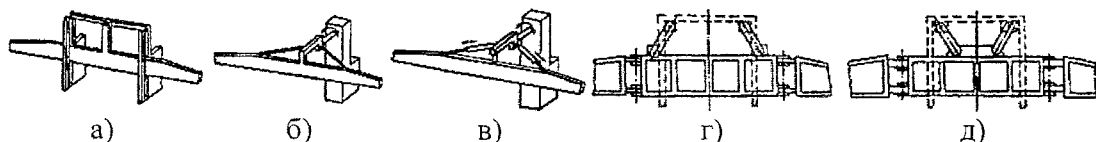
Подвески несущих конструкций штанг к раме опрыскивателя:
